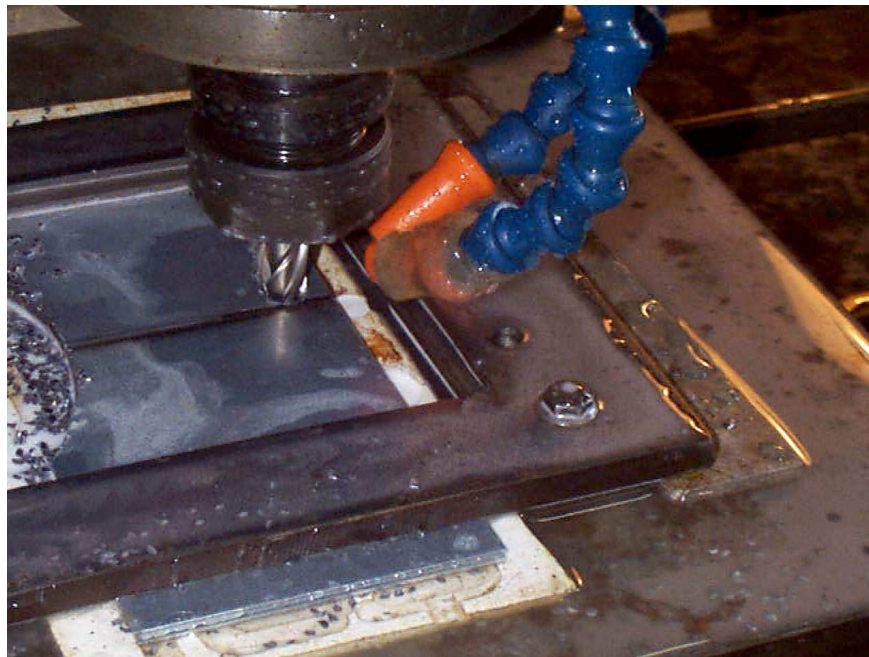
Usinagem de um corpo de prova para o levantamento da CLC de uma chapa soldada.
